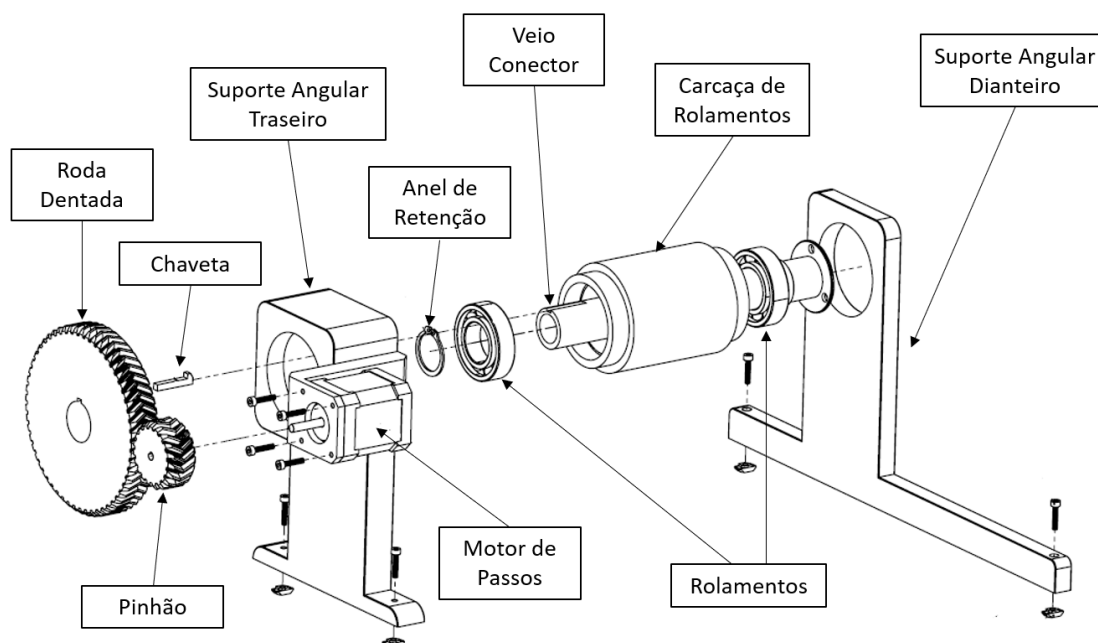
Vista explodida do Suporte angular inicialmente proposto
